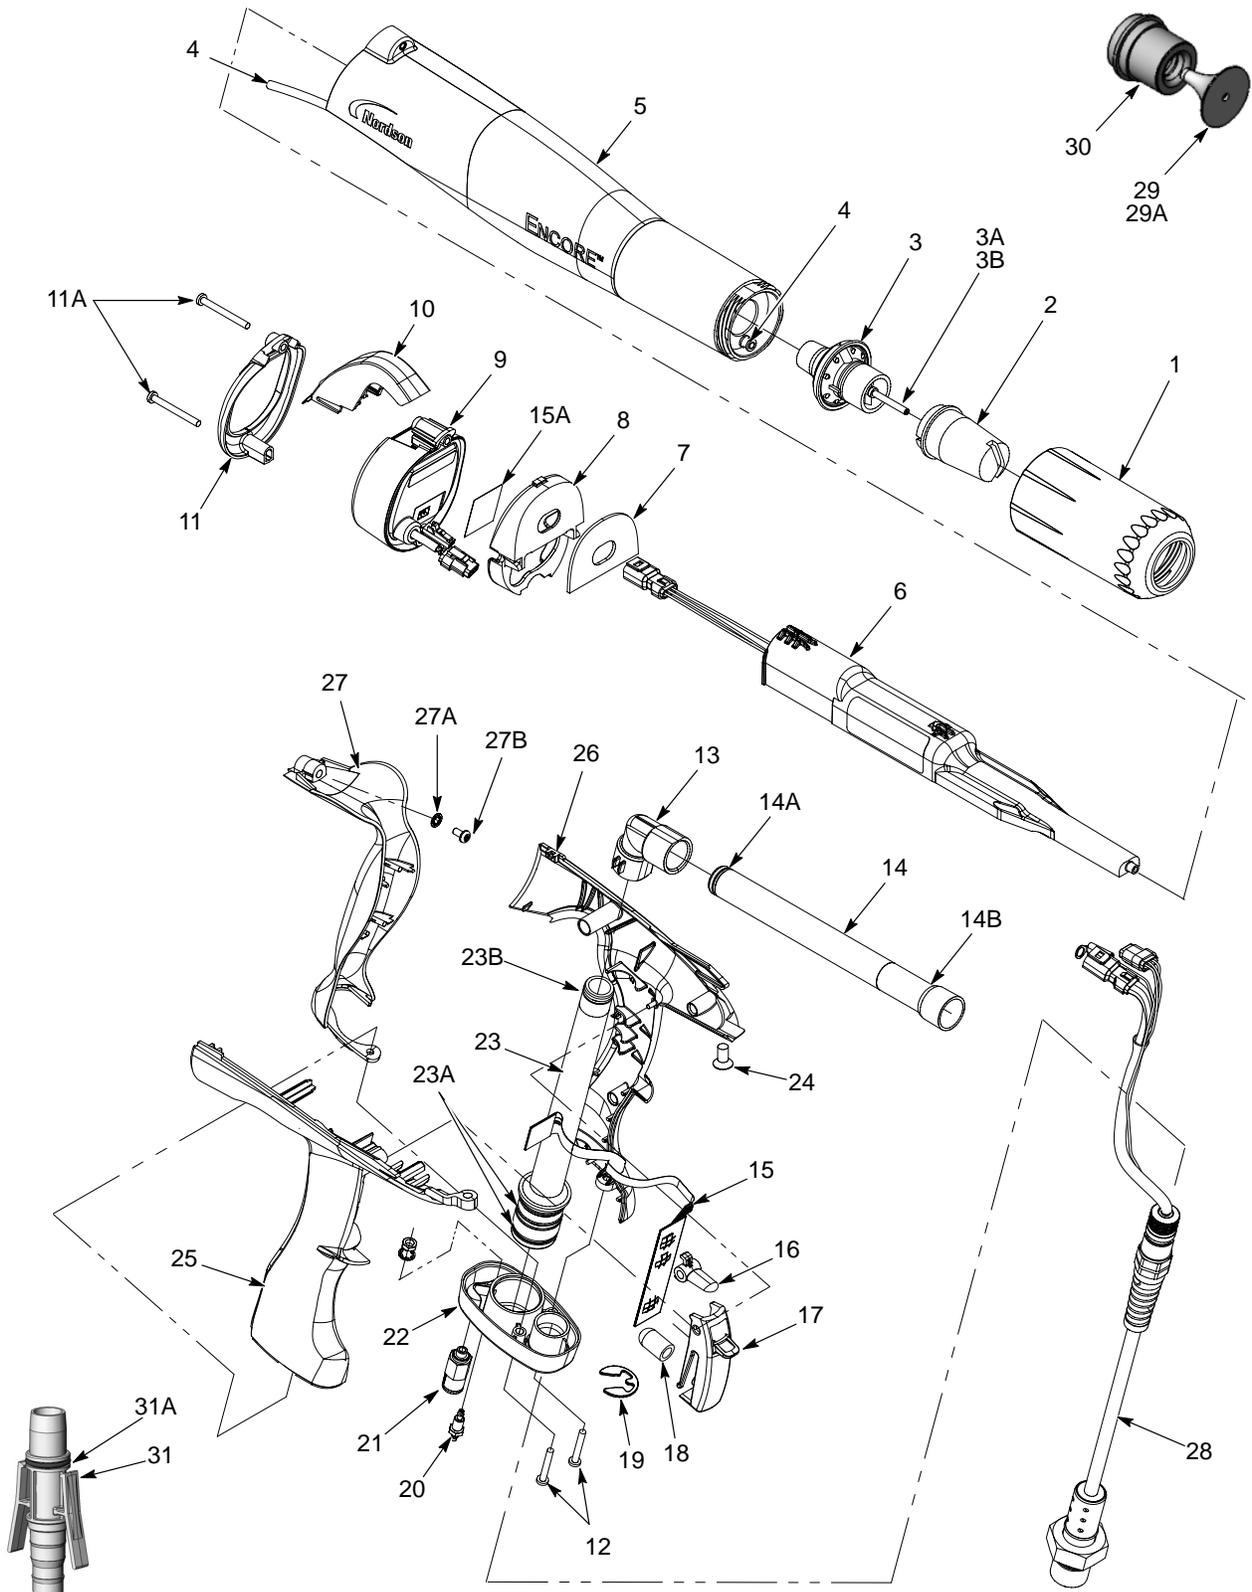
Vista explodida da pistola manual para pintura Encore e acessórios
